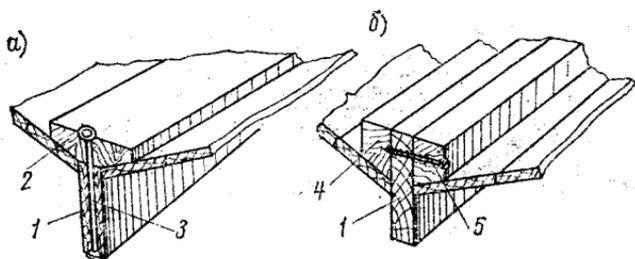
Варианты сборки кия: а — с резенкилем из доски; б — с боковыми рейками.
